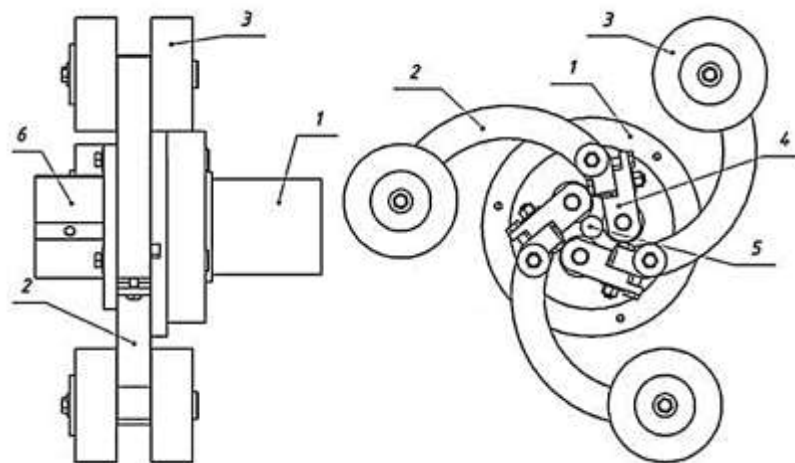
Відцентровий обкатник: 1 - корпус; 2 - важіль; 3 - вантаж; 4 - державка з деформуючим роликом; 5 - обкатувати деталь; 6 – додаткова опора (захисний кожух прибраний).
